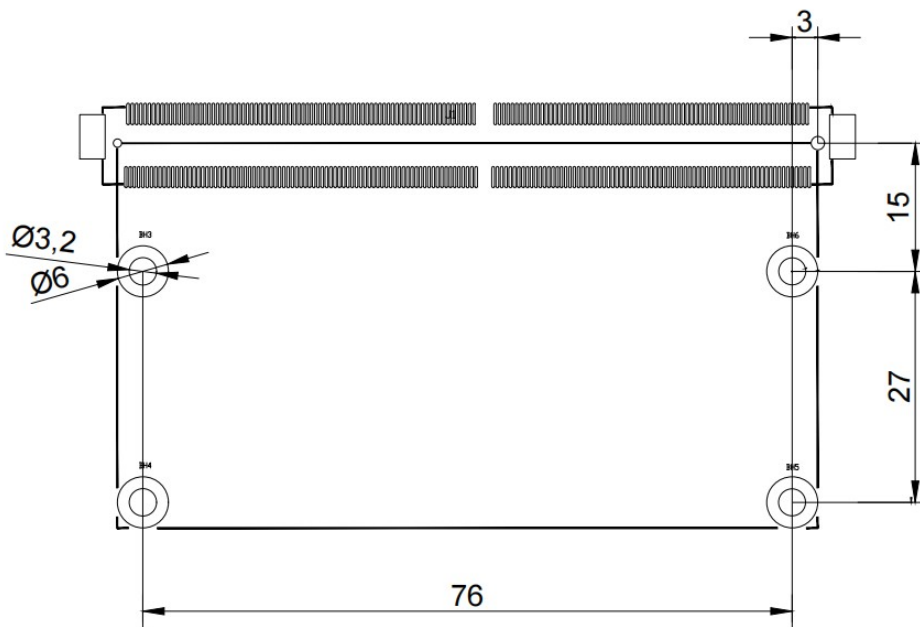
PCB 铜柱固定孔封装尺寸介绍
